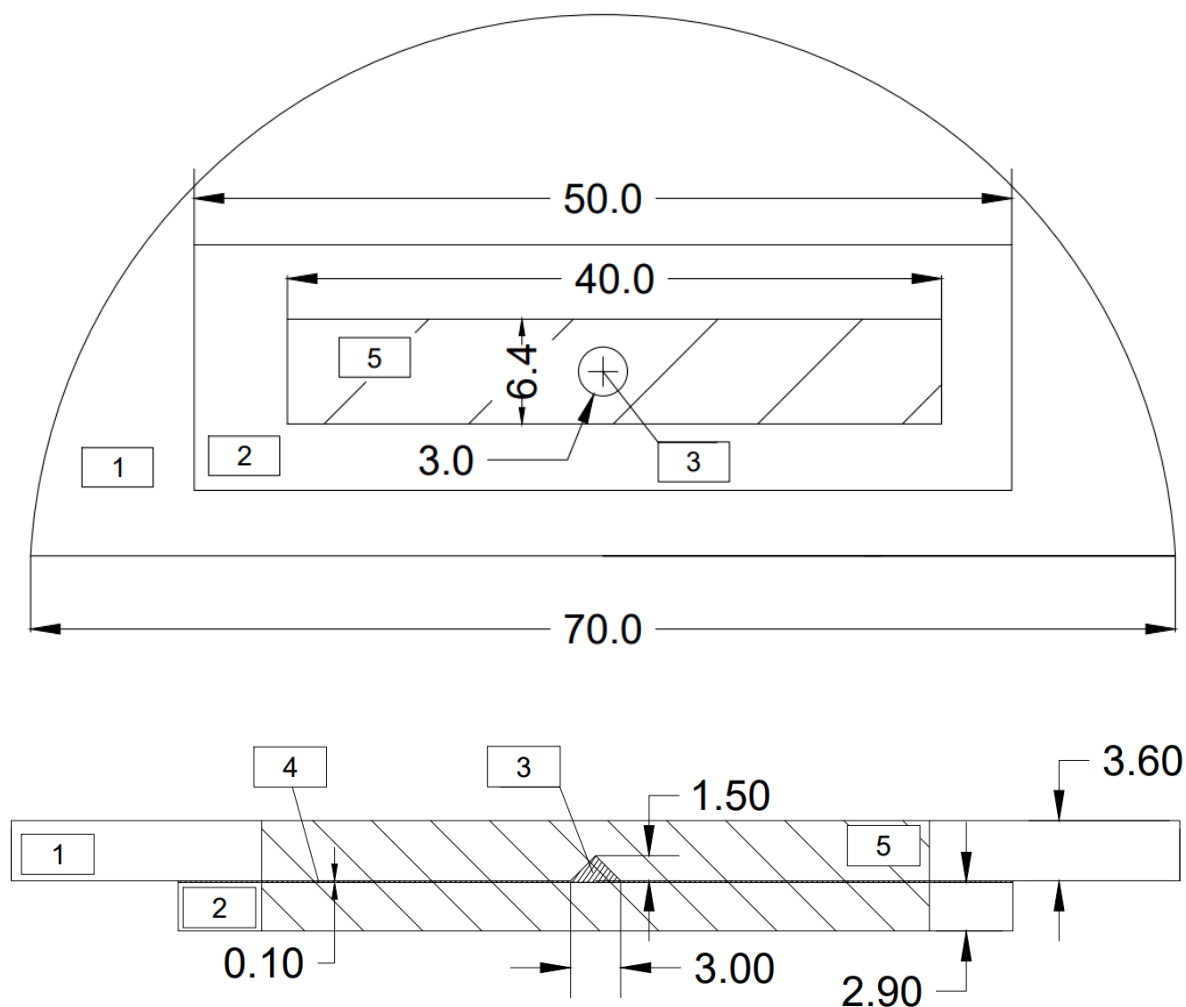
Схема образца АСМ: а - вид сверху; б – вид сбоку.
